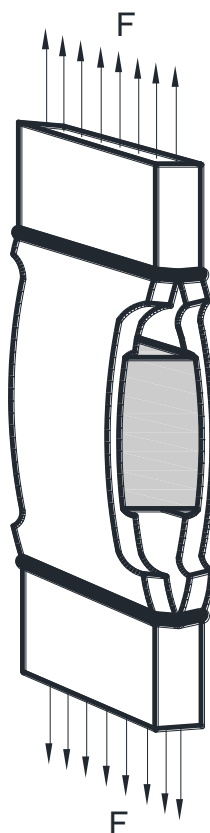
Конструкция испытательного образца с дополнительными выточками
